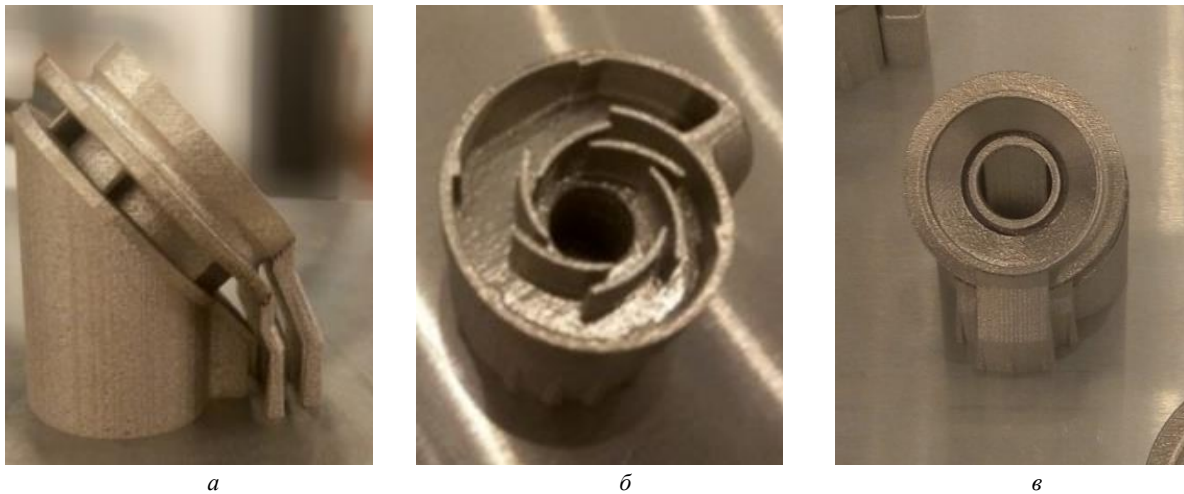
Авіаційна деталь «Завихрувач», отримана шляхом механічної обробки: *а* – вид деталі збоку; *б* – вид деталі зверху; *в* – вид деталі спереду
